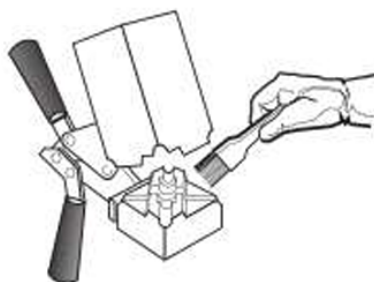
Eliminar los restos de la cámara de soldadura por medio de la brocha
